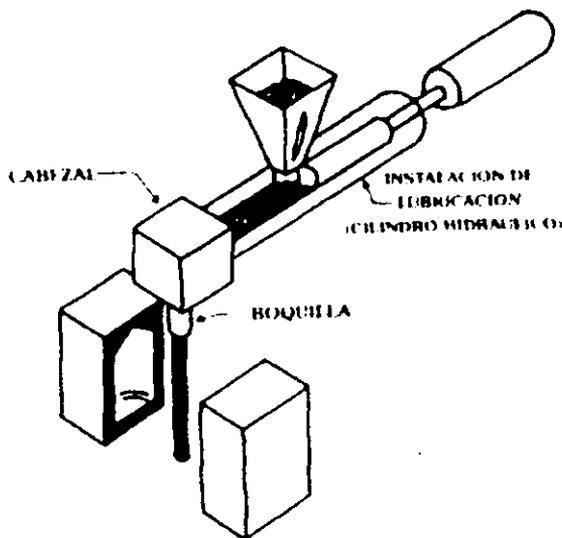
MÁQUINA TÍPICA POR MOLDEO SOPLADO.
